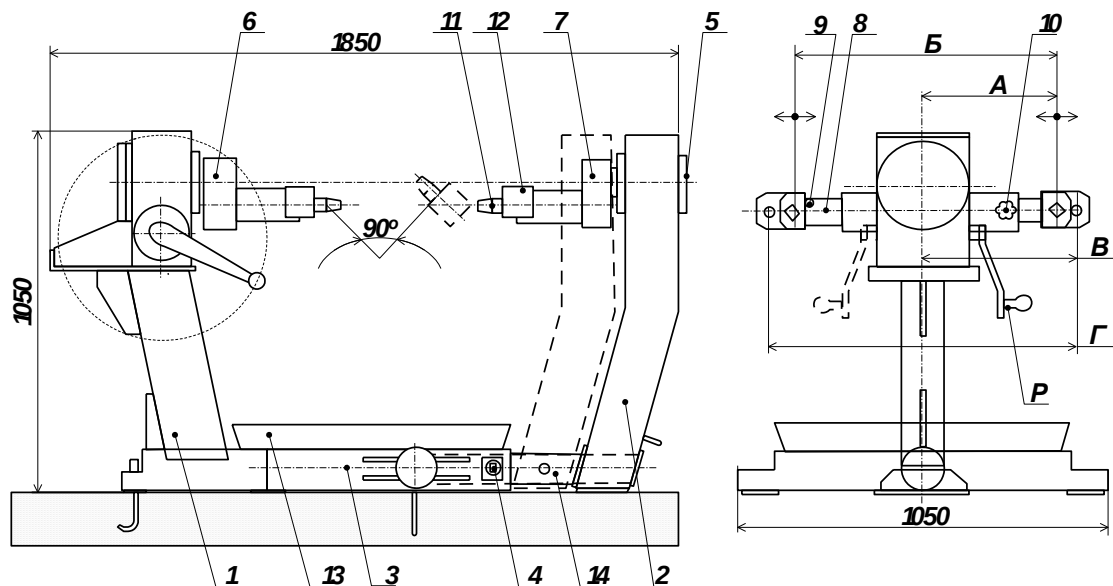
Стенд Р776: 1 – стаціонарна стійка з редуктором; 2 – пересувна стійка; 3 – хрестовина; 4 – фіксатор стійки; 5 – підшипникова опора; 6 – траверса; 7 – траверса; 8 – розсувна опора (4 шт.); 9 – шпонка (4 шт.); 10 – фіксатор опори (4 шт.); 11 – штир (4 шт.); 12 – гвинт (4 шт.); 13 – піддон; 14 – скалка; 15 – електродвигун; 16 – редуктор першого ступеня; 17 – електрошафа управління; 18 – автоматичний вимикач; 19 – лампа індикації увімкнення мережевого живлення; 20 – кнопка увімкнення обертання за годинниковою стрілкою; 21 – кнопка увімкнення обертання проти годинникової стрілки; 22 – заземлюючий пристрій; Р – рукоятка повороту двигуна (90° – 13 обертів рукоятки).
